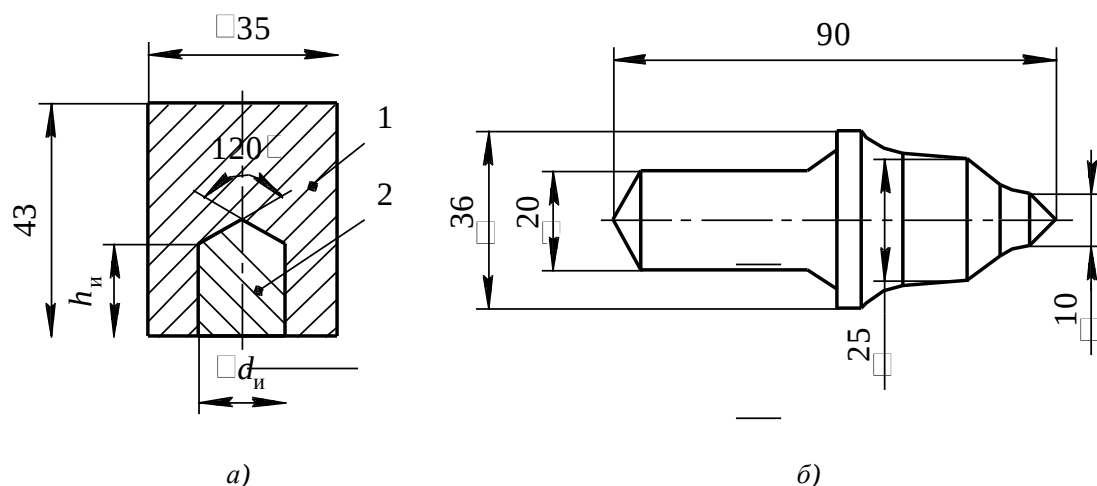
Биметаллическая составная заготовка (а) и эскиз резца после штамповки (б): 1 – металлический корпус; 2 – рабочая вставка; d_u – исходный диаметр рабочей вставки; h_u – исходная высота рабочей вставки
